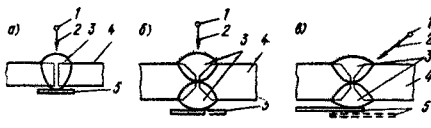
Схемы испытания швов стыковых сварных соединений с различным направлением центрального луча
